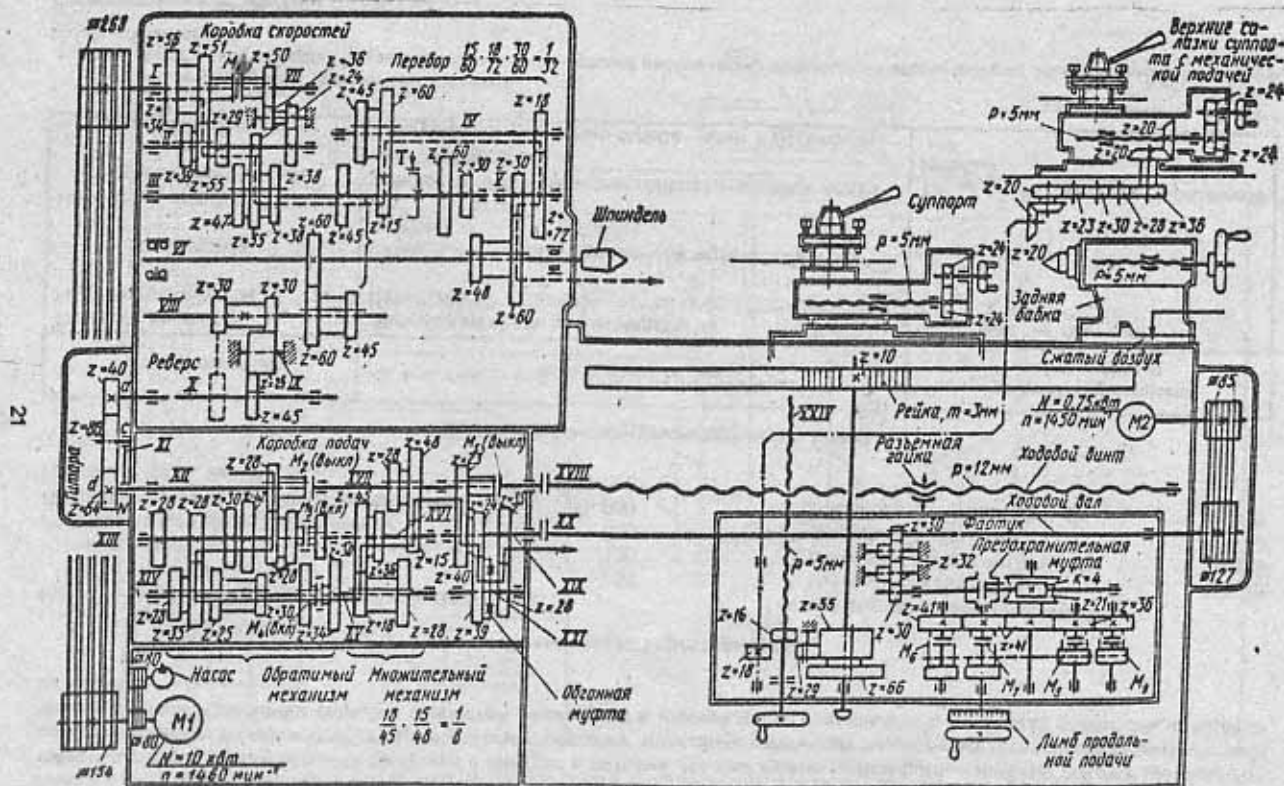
Кинематическая схема токарно-винторезного станка мод. 16К20
